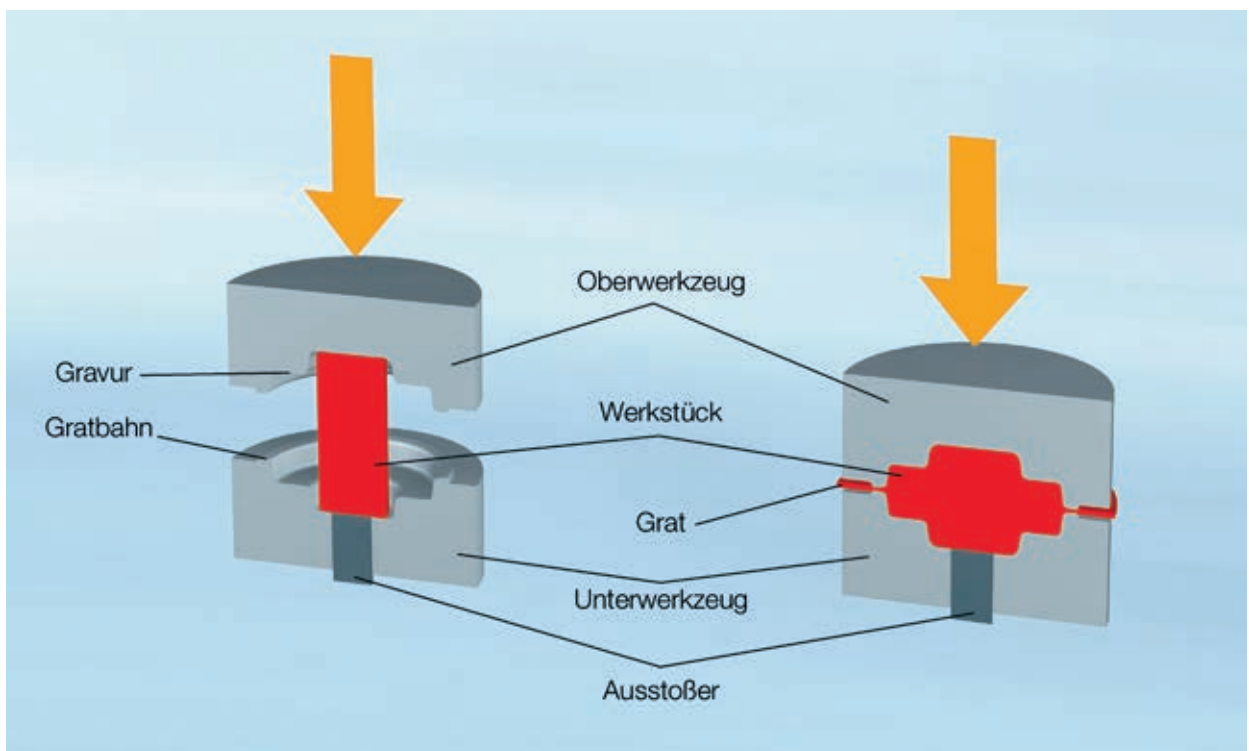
Gesenkschmieden (Gesenkformen) mit Grat
